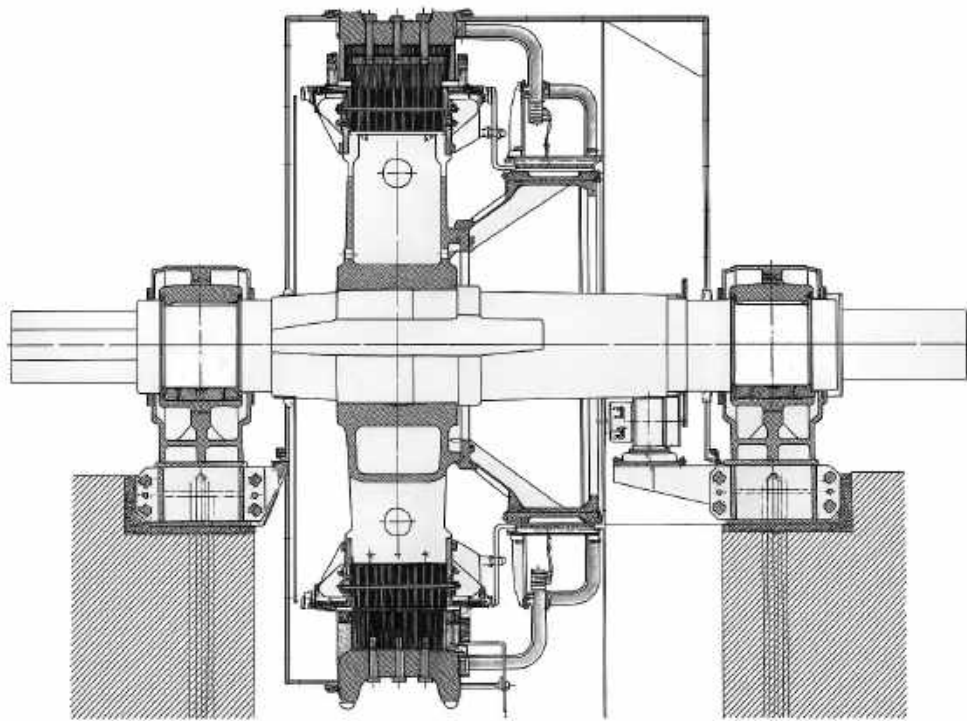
Реверсивний електродвигун прокатного стану
